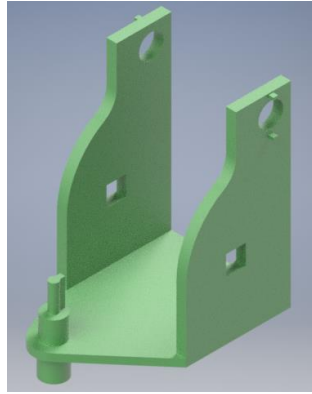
Versión 1.0. Diseño del soporte y ensamblaje soporte 1.0 - dedo 2.0 .
